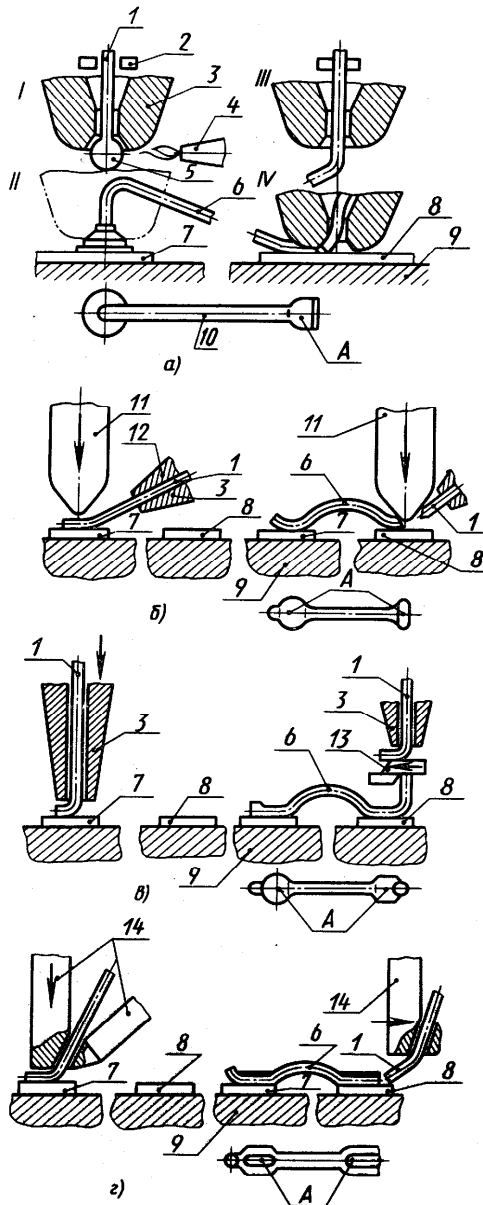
Виды термокомпрессионной сварки выводов
